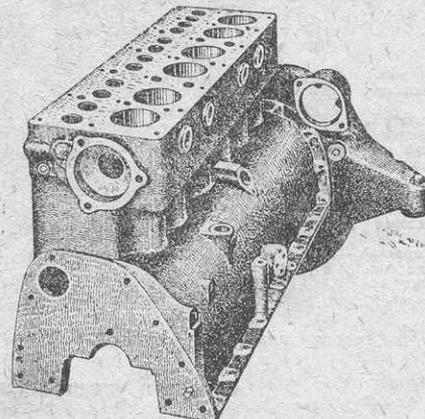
Блок цилиндров, отлитый заодно с верхней частью картера. Головка цилиндров снята (двигатель автомобиля Окланд).
